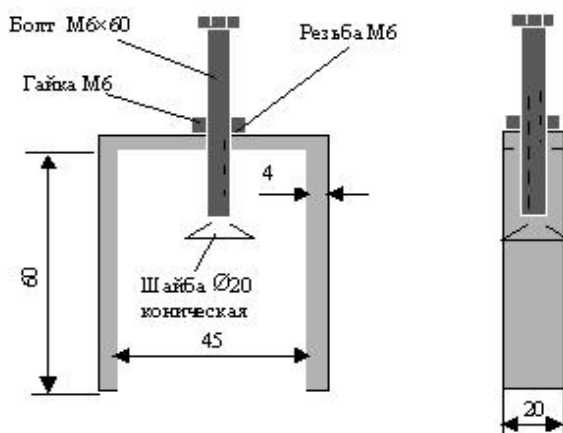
Скоба для крепления накладных ПЭА на трубопроводе
